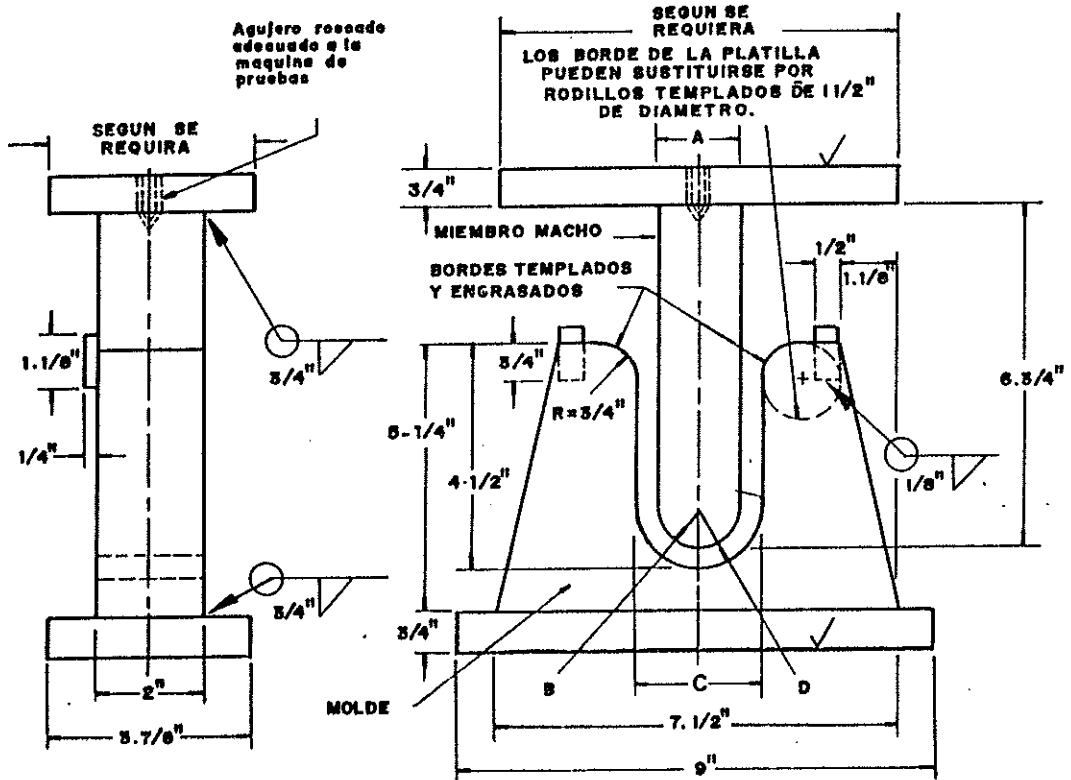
Máquina estándar para prueba de doblado guiado, según AWS D1.1
